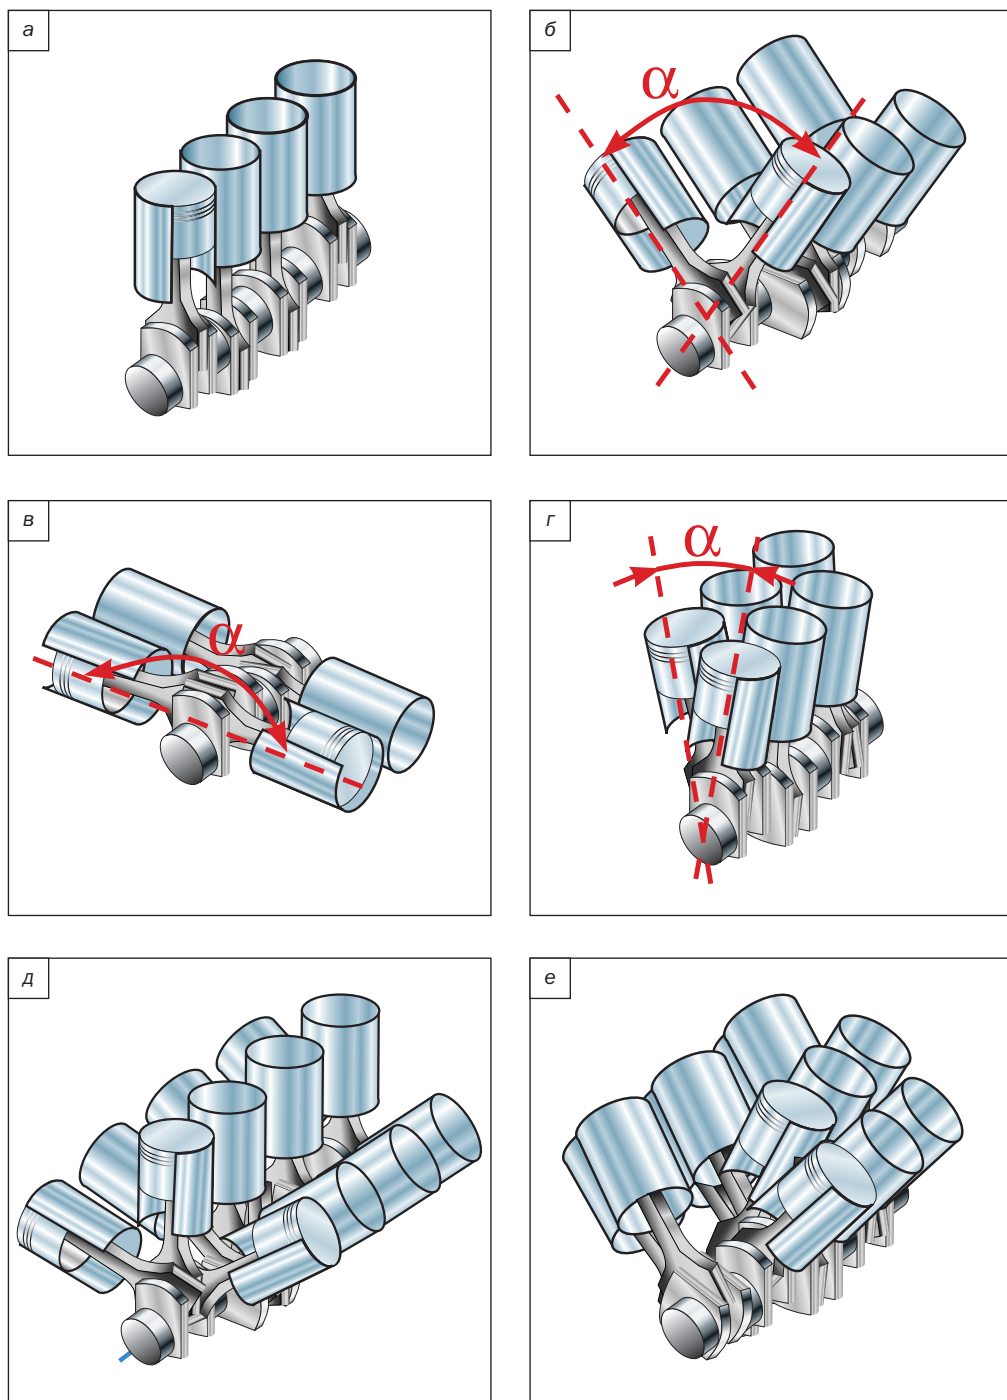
Схемы расположения цилиндров в двигателях различной компоновки: а — рядный четырехцилиндровый; б — V-образный шестицилиндровый; в — оппозитный четырехцилиндровый; г — VR-двигатель шестицилиндровый; д и е — W-образные 12-цилиндровые двигатели; α — угол развала
